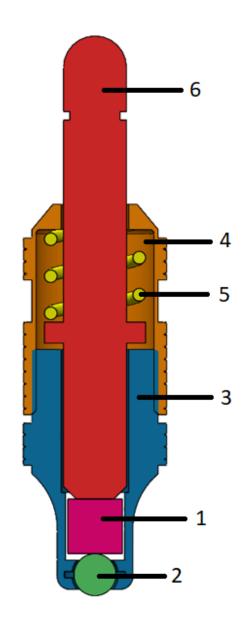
Вид с разрезом: 1 — контрольный брусок, 2 — шарик, 3 — державка, 4 — крышка, 5 — пружина, 6 — боек
